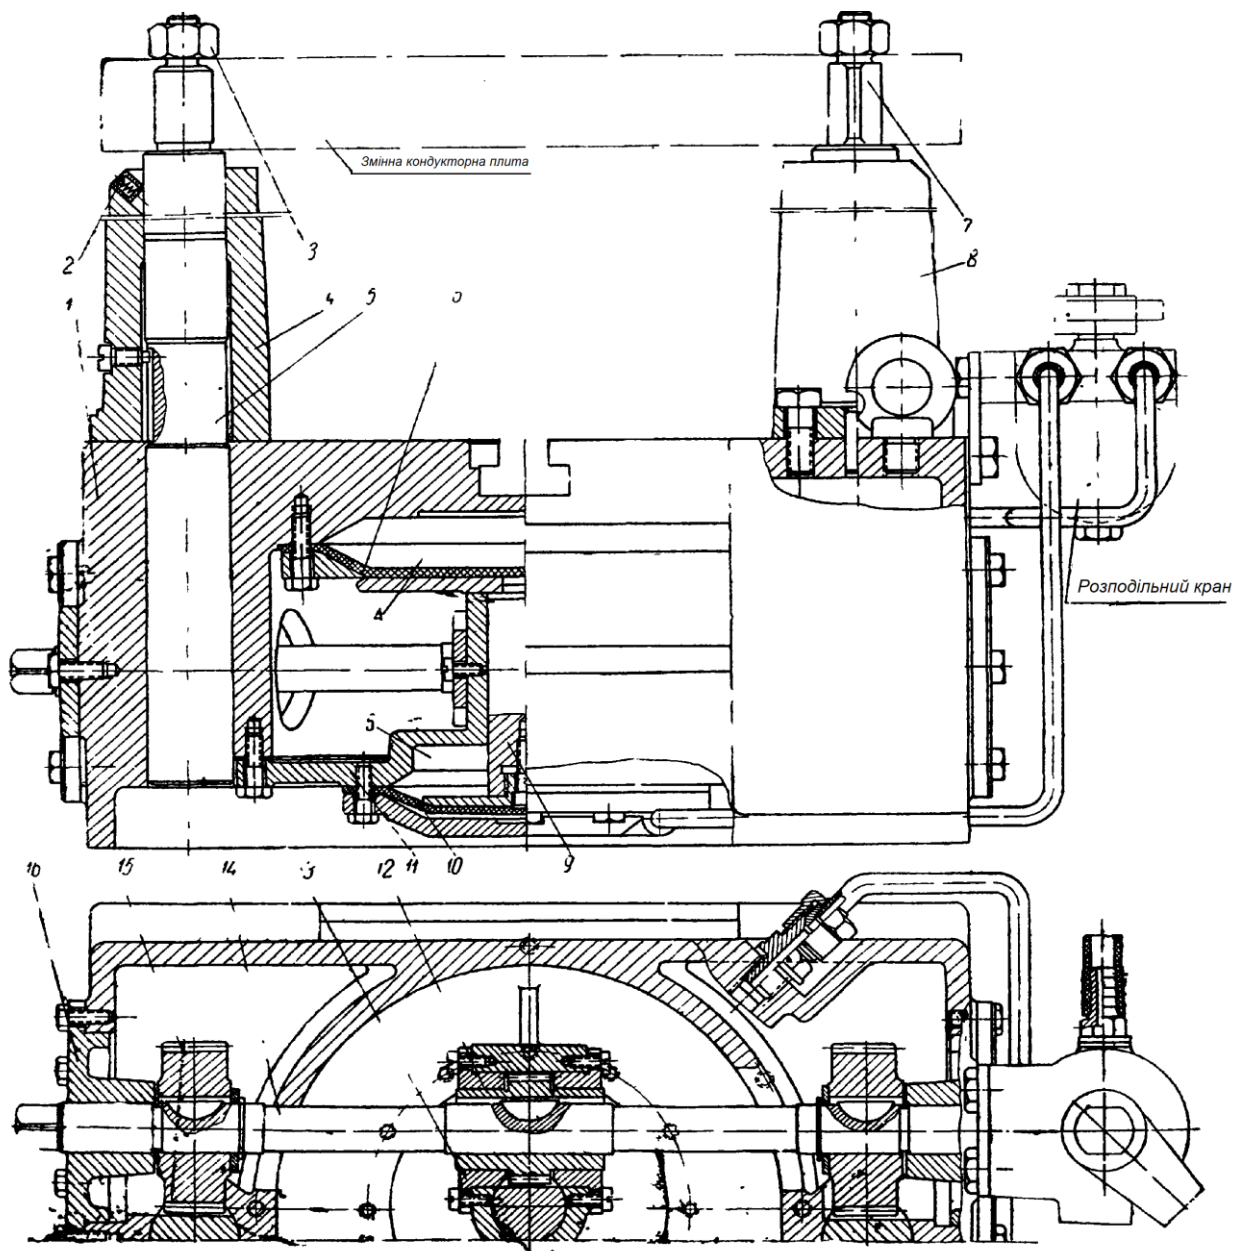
Скальчастий кондуктор порталного типу з пневматичним приводом
